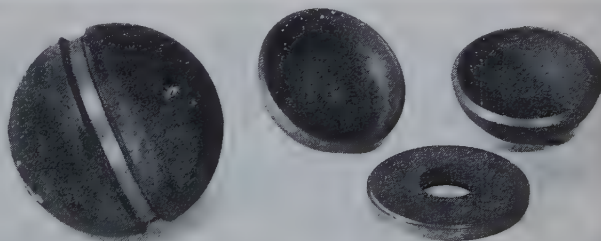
Hohlkugel, bestehend aus 2 gepreßten Halbschalen und eingelegter Zwischenscheibe mit Einzelteilen, fertig zum Verschweißen
